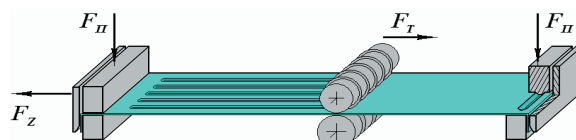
Способ изготовления профилей с плоскими концевыми участками
